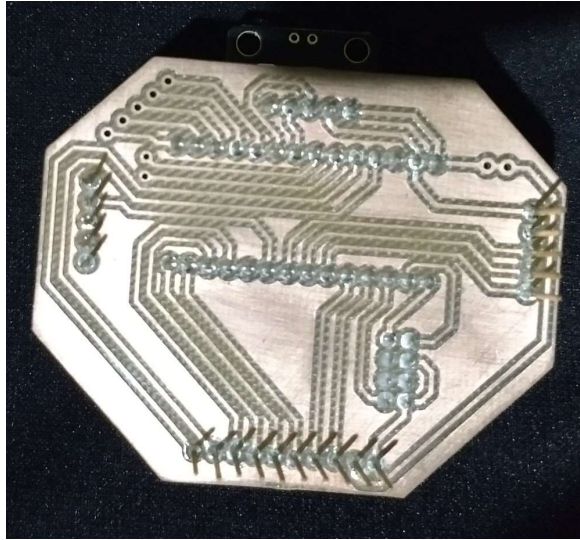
PCB de módulos montado sobre PCB de sensores ultrasónicos.
